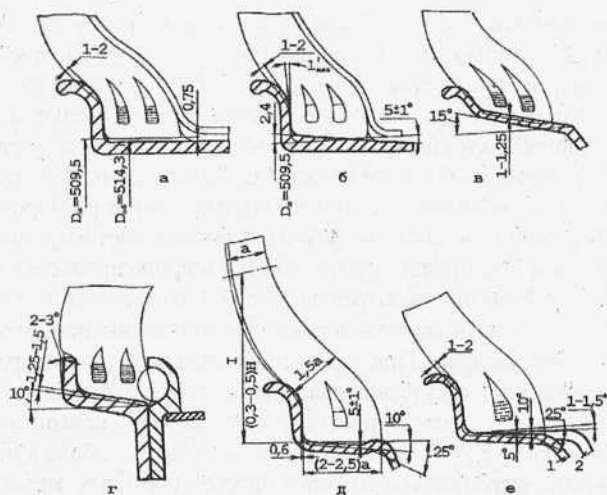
Бортовые закраины ободьев: I – зона усиления; а – г – для грузовых автомобилей; д, е – для легковых автомобилей с бескамерными шинами; а – плоский обод; б – обод с коническими полками; в – глубокий обод для бескамерных шин; г – обод для арочных шин и пневмокатков; д – обод, имеющий посадочную полку с хампом на внешней стороне колеса; е – обод с удлиненной полкой; 1 – полка с внутренней стороны колеса; 2 – полка с внешней стороны колеса; $D_{ш}$ – посадочный диаметр шины; $D_{об}$ – то же обода; Н – высота профиля, а – толщина оболочки
